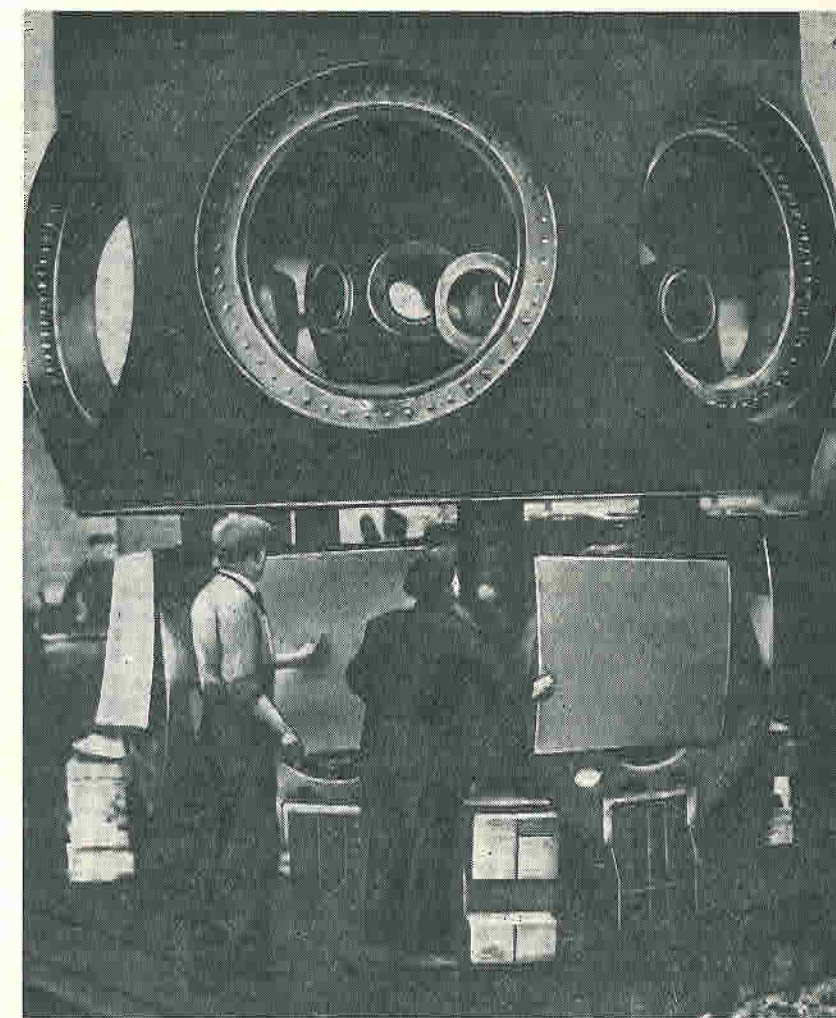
Установка втулки рабочего колеса бескрестовинного типа на сборочную плиту с закрепленными на приспособлении рычагами
